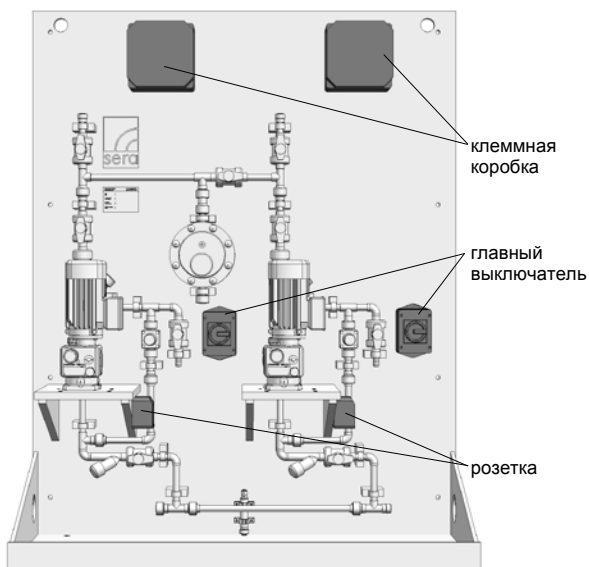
Опция клеммная коробка, розетка и главный выключатель
